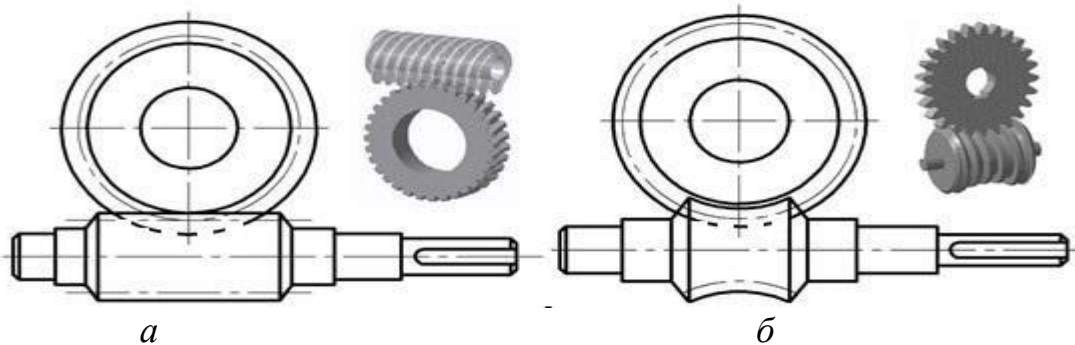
Форми зовнішньої поверхні черв'яка
